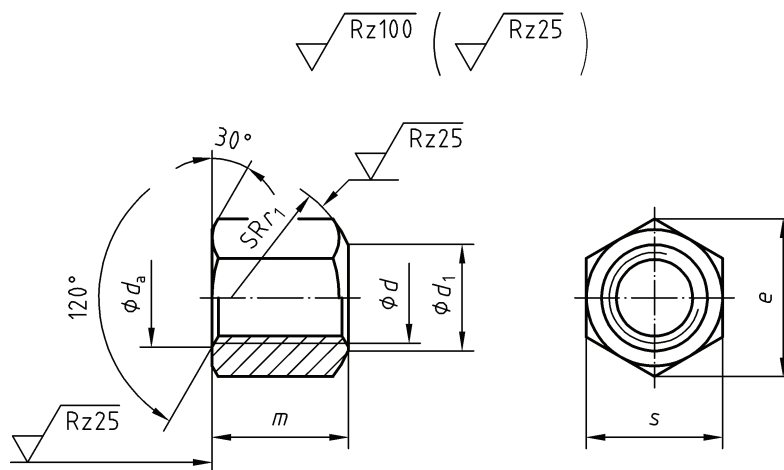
Sechskantmutter Form B, mit einseitig kugelliger Auflagefläche
